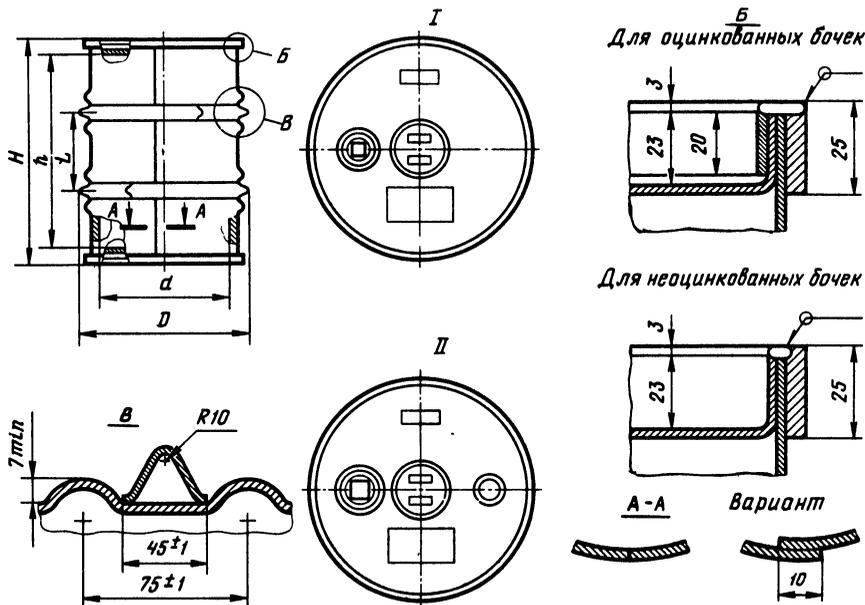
Бочки стальные сварные с обручами катания на обечайке
